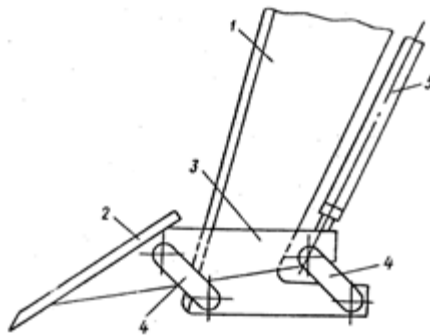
Рабочий шарнирно – соединенный орган рыхлителя
